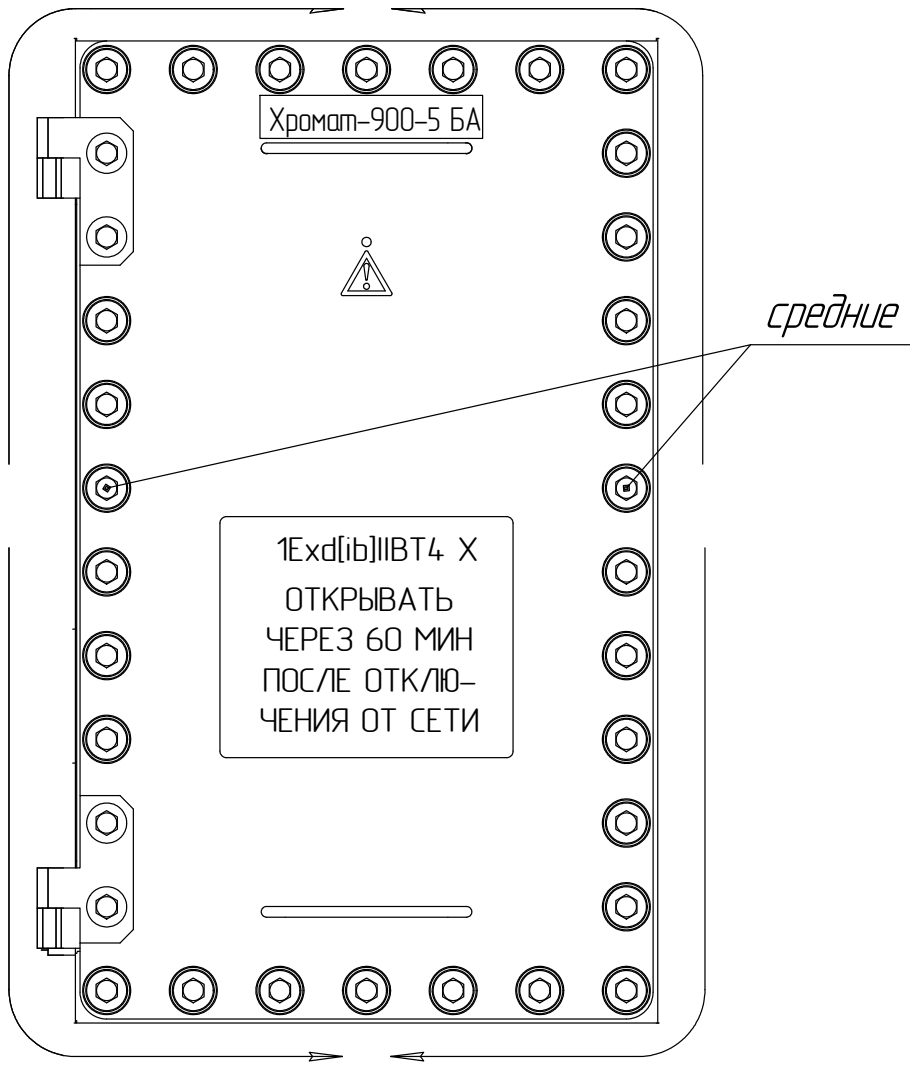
Порядок закрытия крышки оболочки БА
